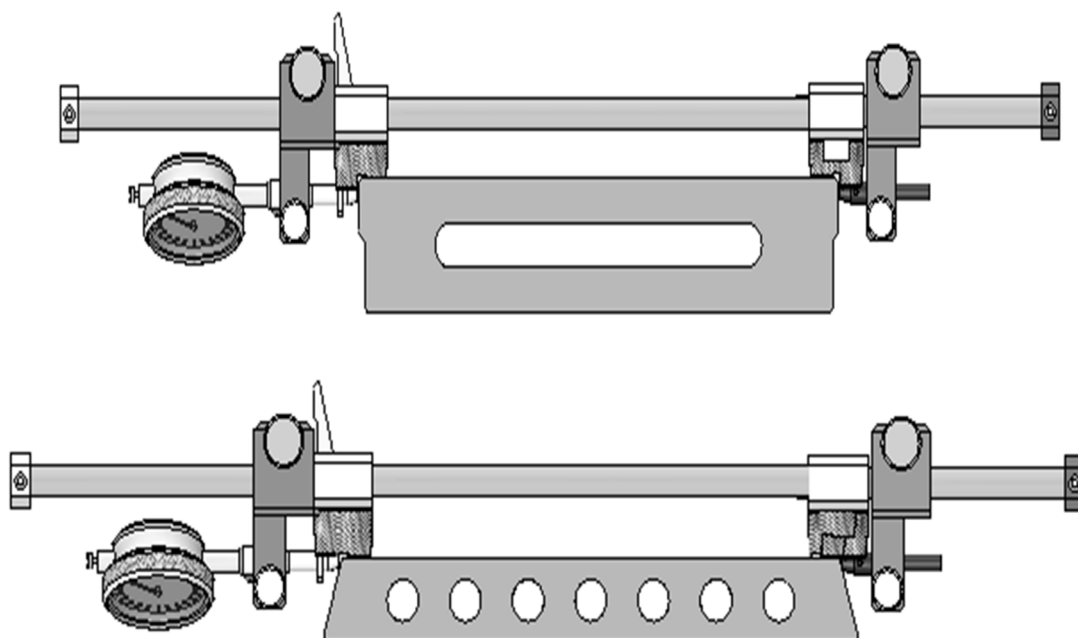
б – Схема настройки индикаторного прибора со ступенчатыми поворотными упорами для измерения диаметра уплотнительной проточки трубы в измерительной плоскости по специальному настройчному шаблону
